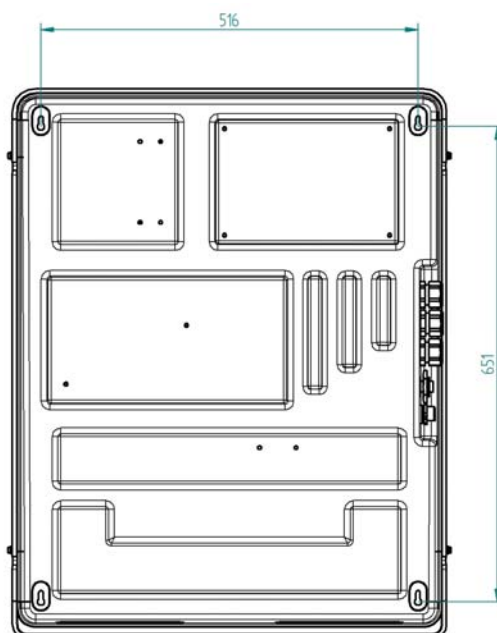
Placa NEXT para instalación en la pared (dimensiones en mm).
